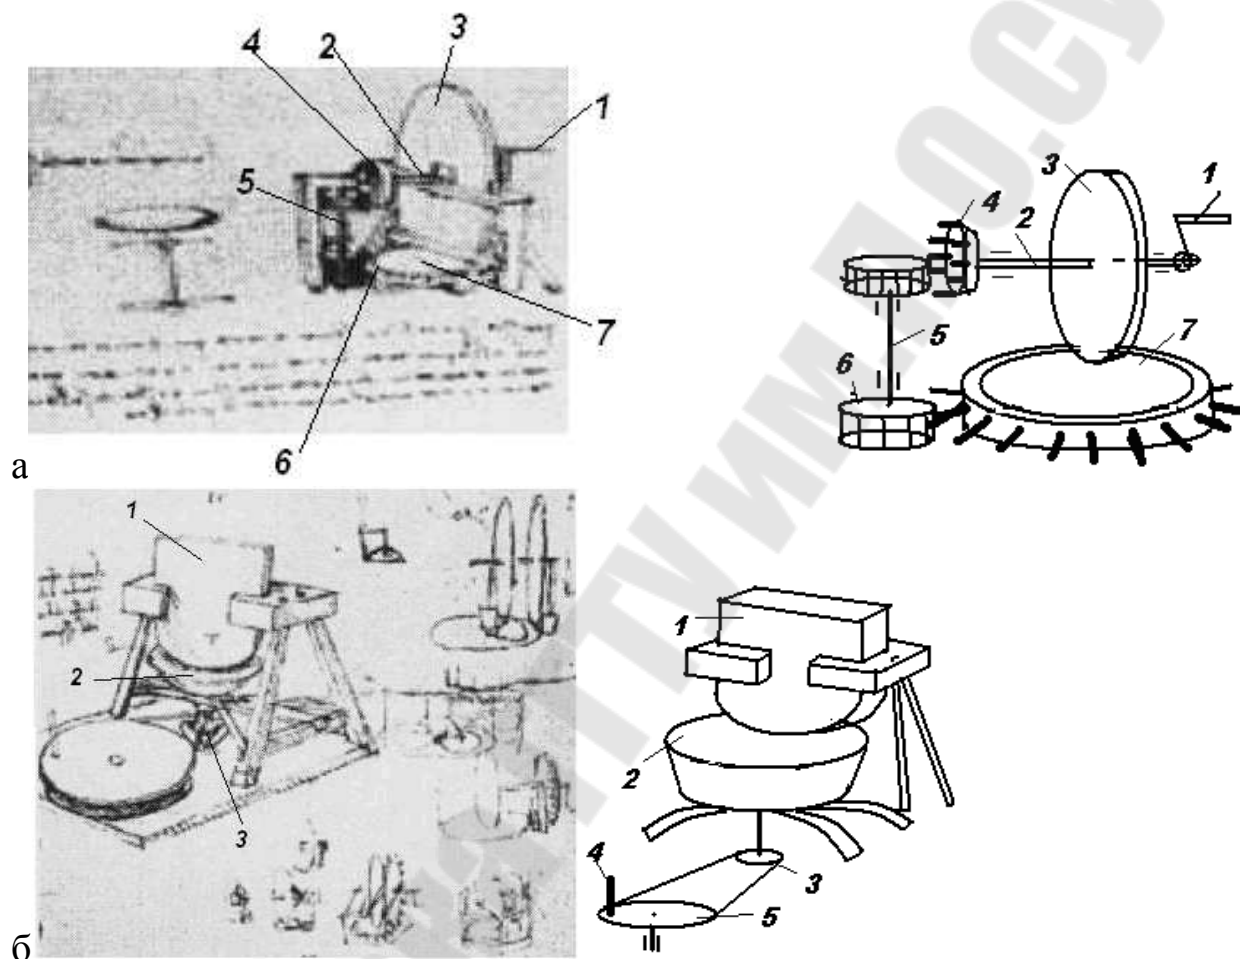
Рисунки Леонардо да Винчи станков для обработки зеркал : вращающимся абразивным диском (а) и неподвижным абразивным камнем (б)
